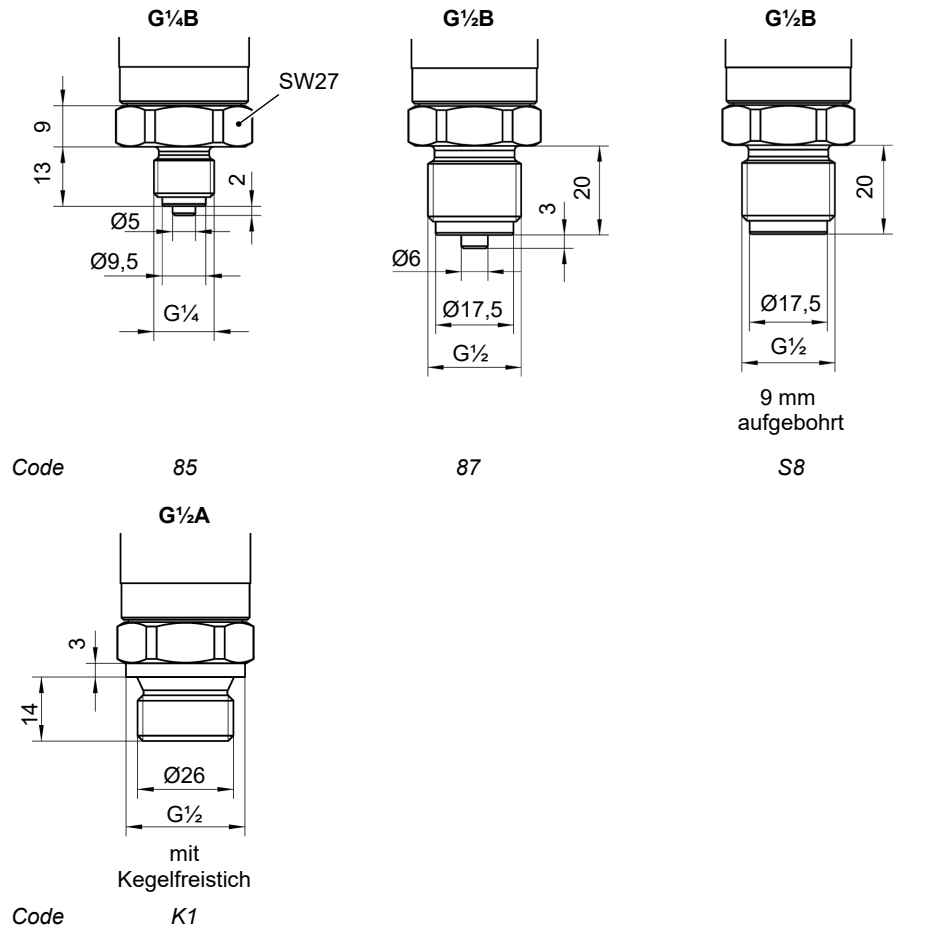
Prozessanschlüsse mit zölligem Gewinde
